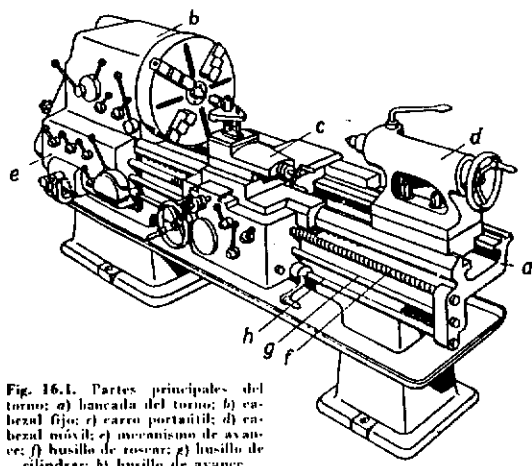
Partes principales del torno: a) bancada del torno; b) cabezal fijo; c) carro portátil; d) cabezal móvil; e) mecanismo de avance; f) husillo de roscar; g) husillo de cilindrar; h) husillo de avance.
